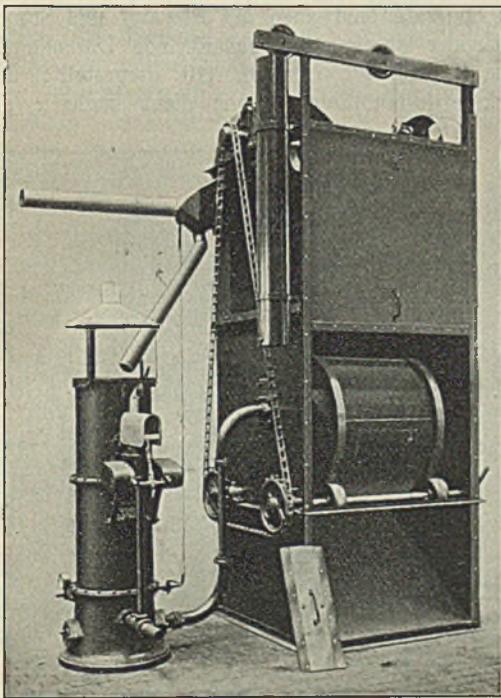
Rotationstrommel mit einer feststehenden Blasdüse, schlauchlos, Bauart Gutmann.
